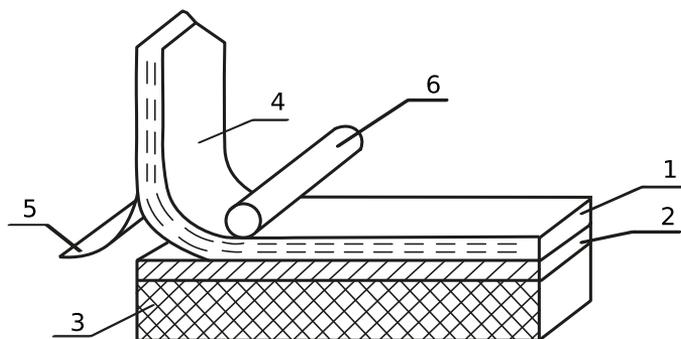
Схема нанесения сухого пленочного фоторезиста на печатную плату
